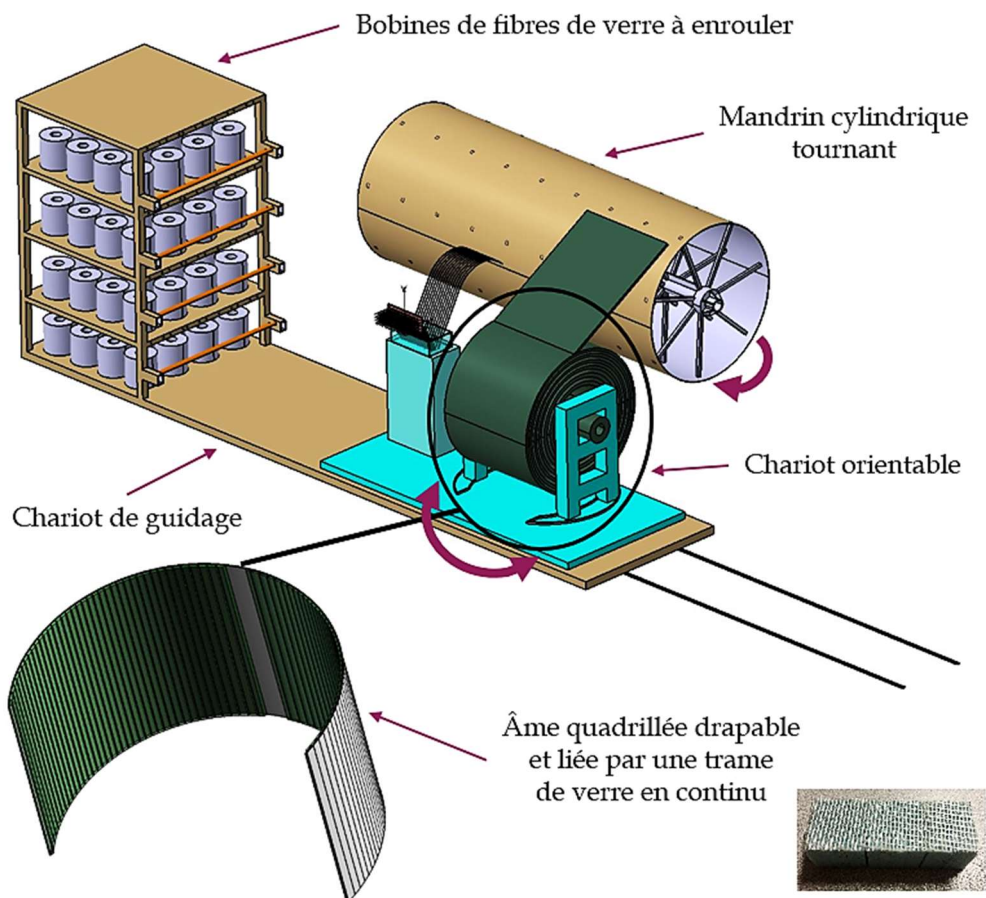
Vue d'ensemble de la solution d'enroulement des bobines d'âme.
